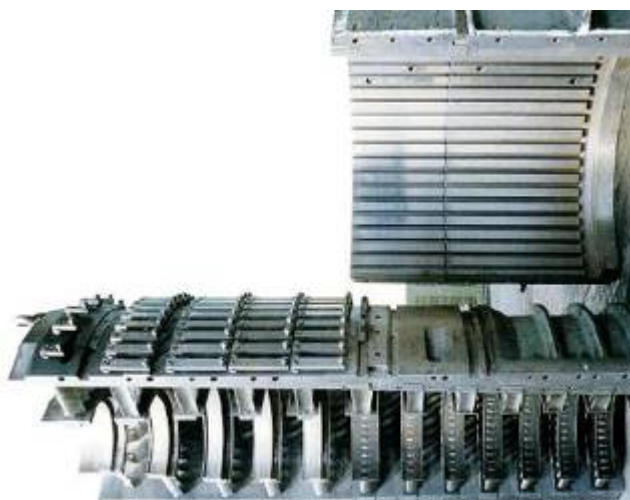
Система управления РНА компрессора двигателя фирмы Роллс-Ройс
